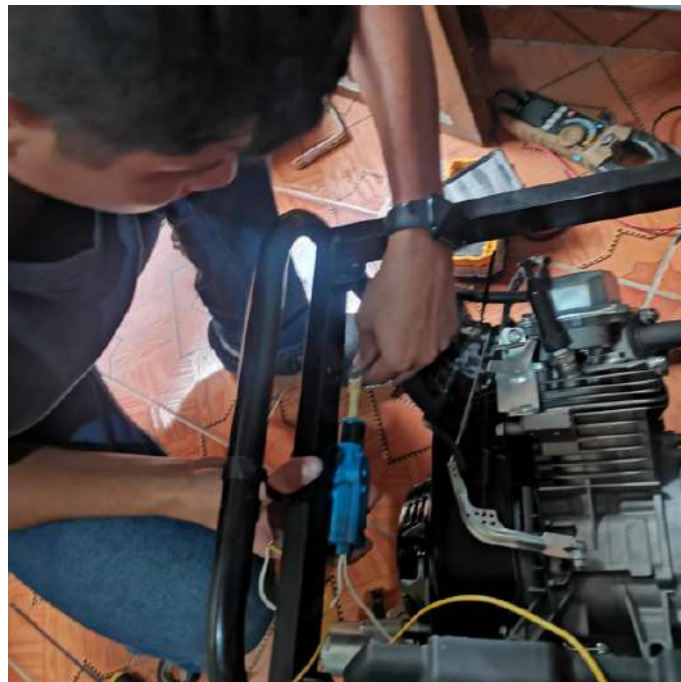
Montaje de sistema de anclaje, cadena y motor de arranque en el cigueñal.
